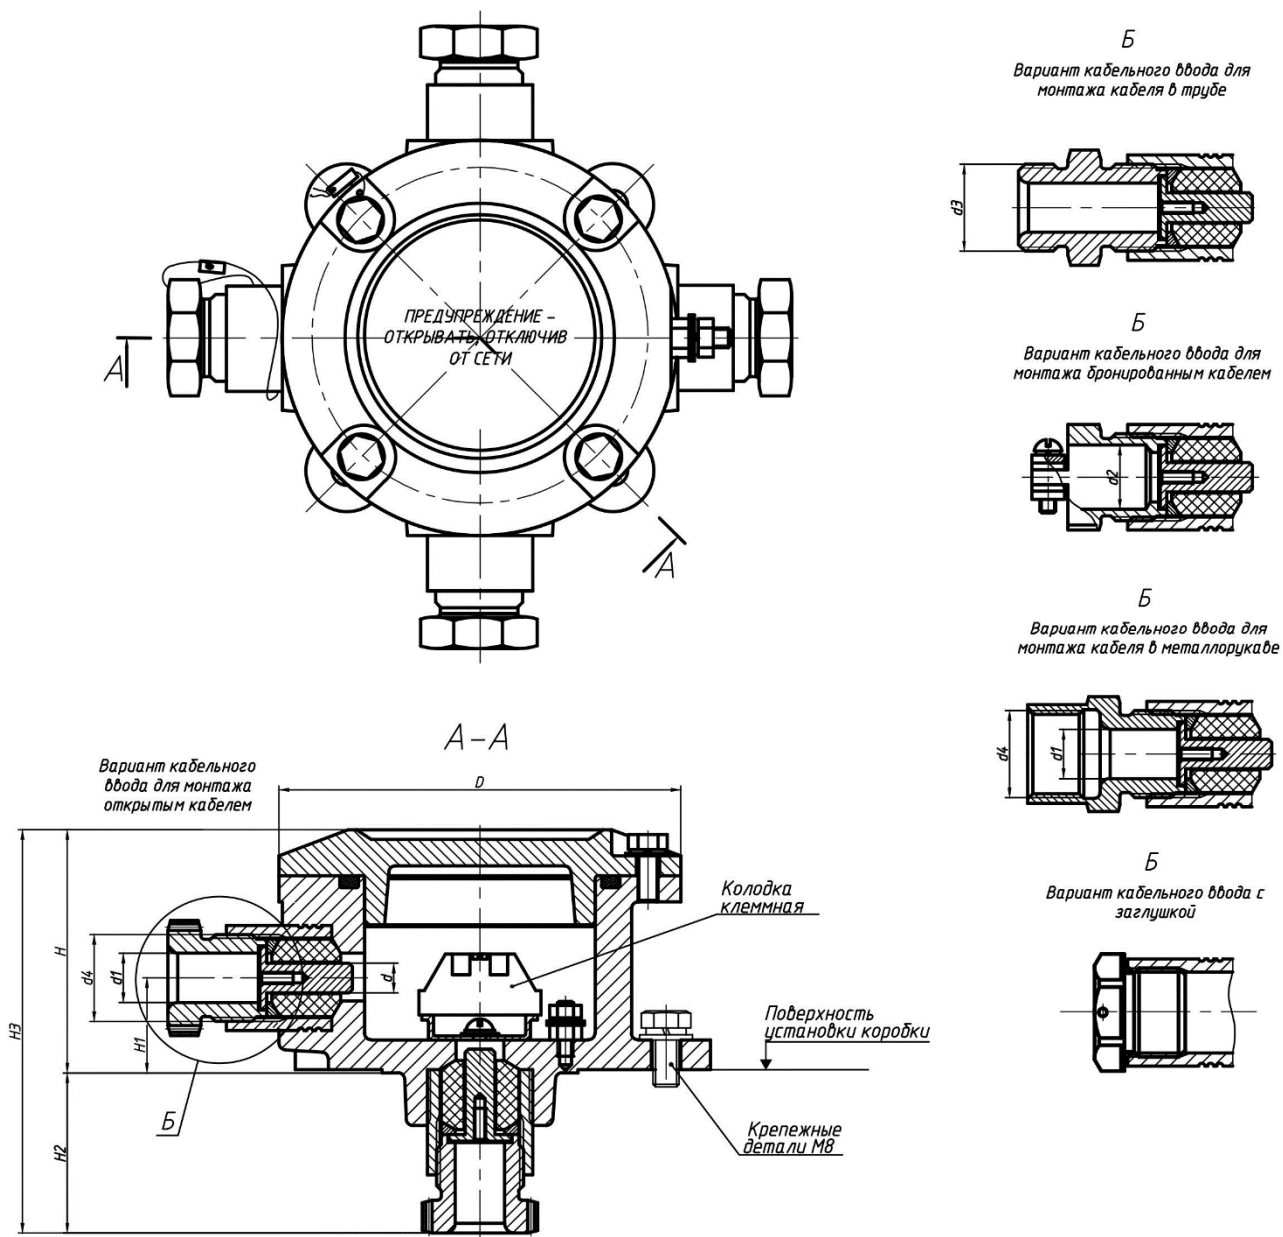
Габаритные, установочные и присоединительные размеры базовой коробки ЕхКСУВ-А
